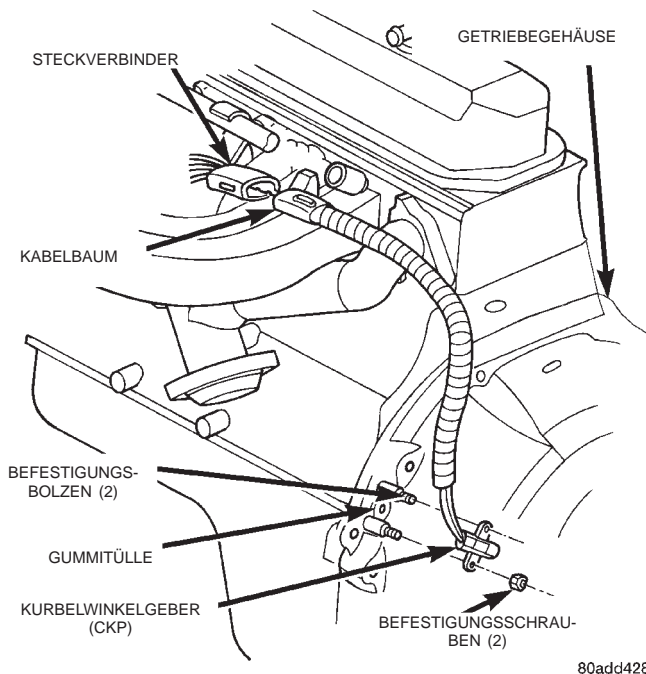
Kurbelwinkelgeber (CKP)—2.5L-Vierzylindermotor—Fahrzeuge mit Automatikgetriebe
